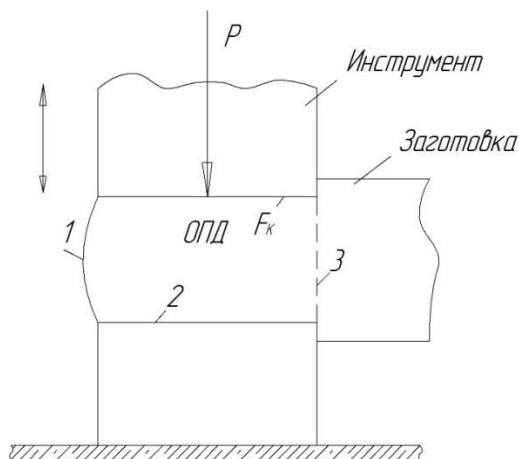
Схема процесса протяжки заготовки на плоских бойках
